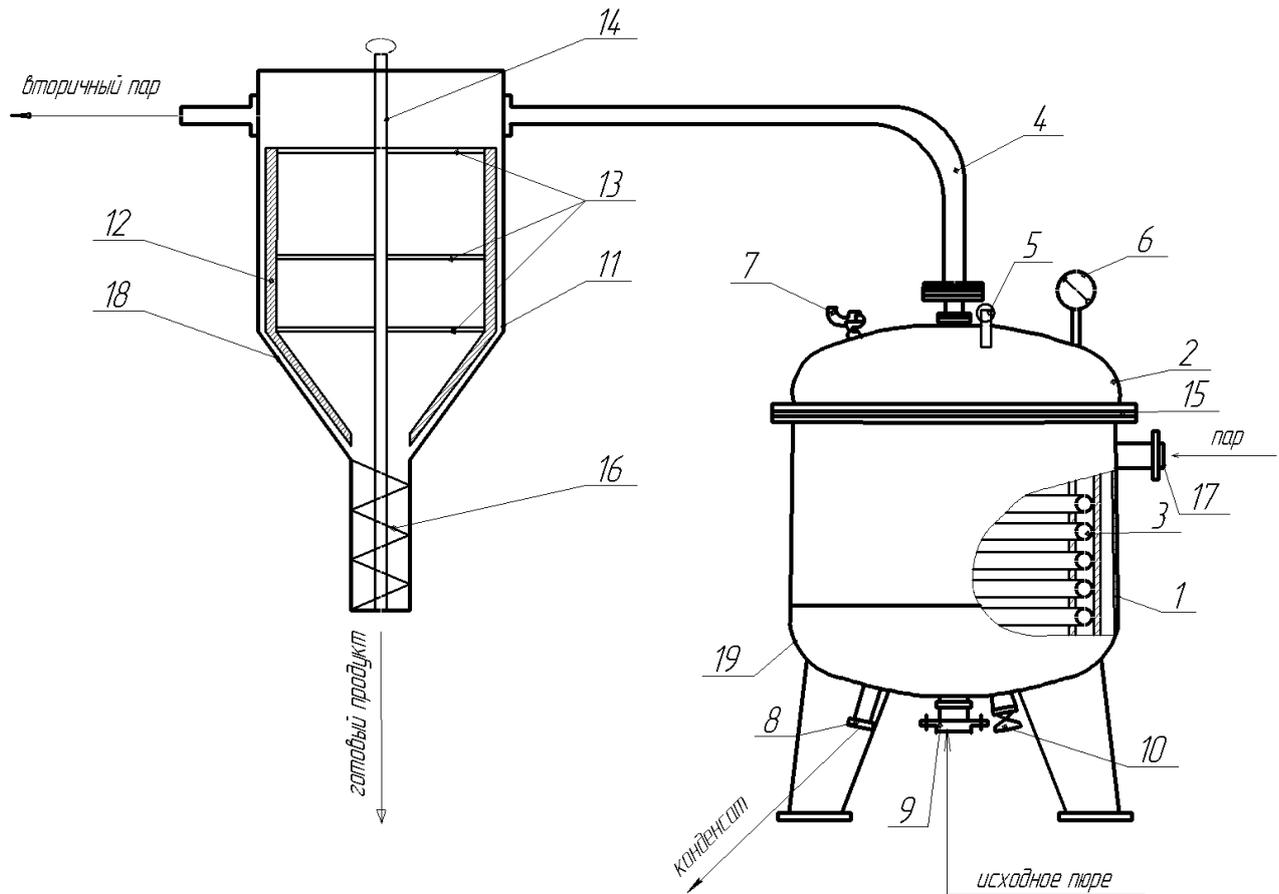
Установки для производства концентрированных паст из фруктово-овощного сырья: 1- корпус; 2- крышка; 3- медный змеевик; 4- соединительный трубопровод; 5- предохранительный клапан; 6- манометр; 7- кран для выпуска воздуха; 8- штуцер для конденсата; 9- входной патрубок; 10- воздушный кран; 11- выпарная камера; 12- лопасти; 13- рама; 14- вал; 15- уплотнитель; 16- шнек – дозатор; 17- штуцер для подачи пара; 18- корпус
